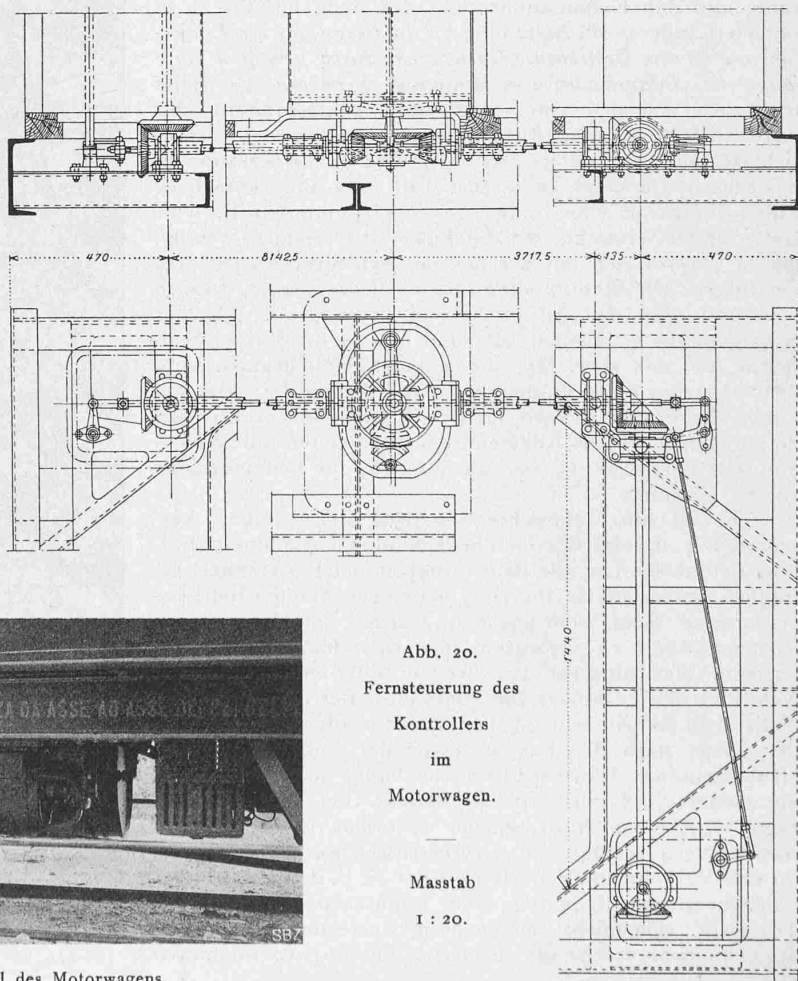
Fernsteuerung des Kontrollers im Motorwagen.
